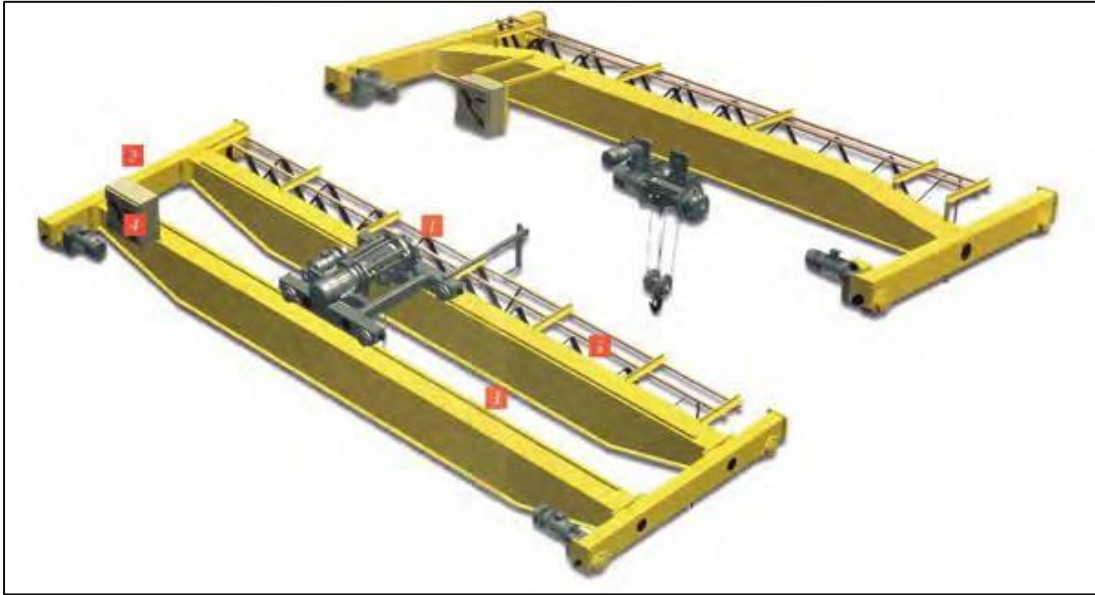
Puente-grúa para las vías de levante y el taller mecánico
